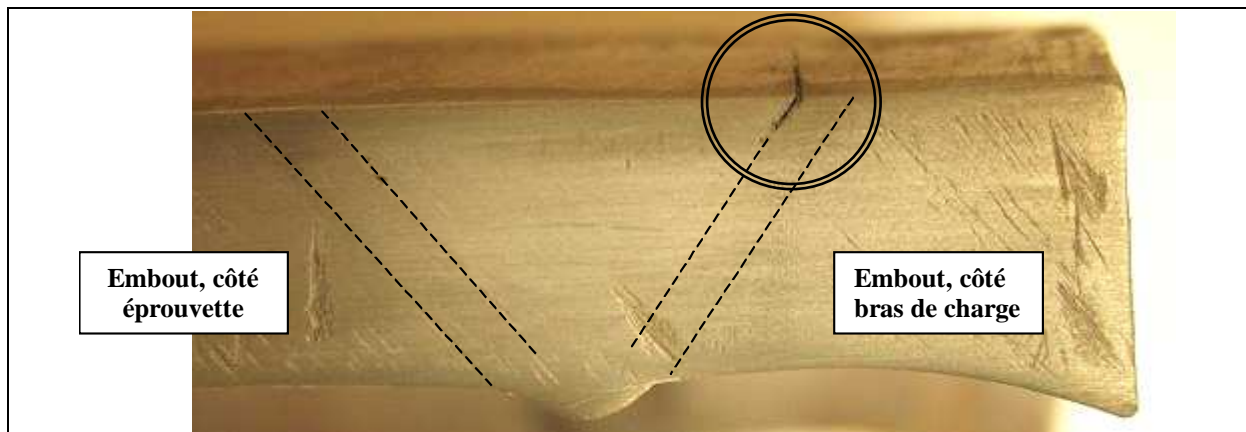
Décollement dans la soudure de l'embout SUD.
